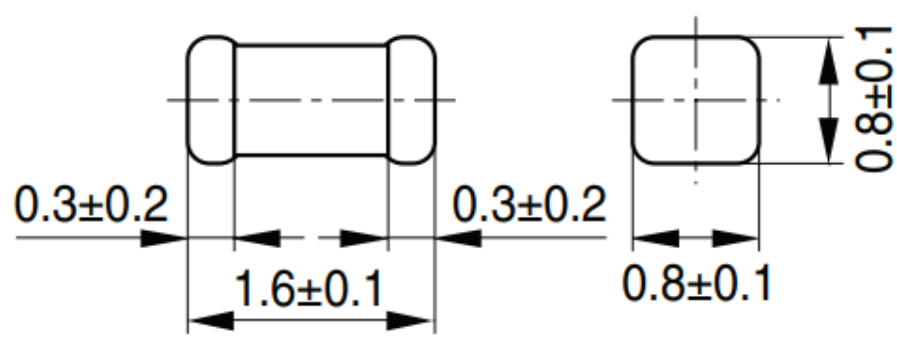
Габаритні розміри котушки індуктивності SIMID 0603-С
